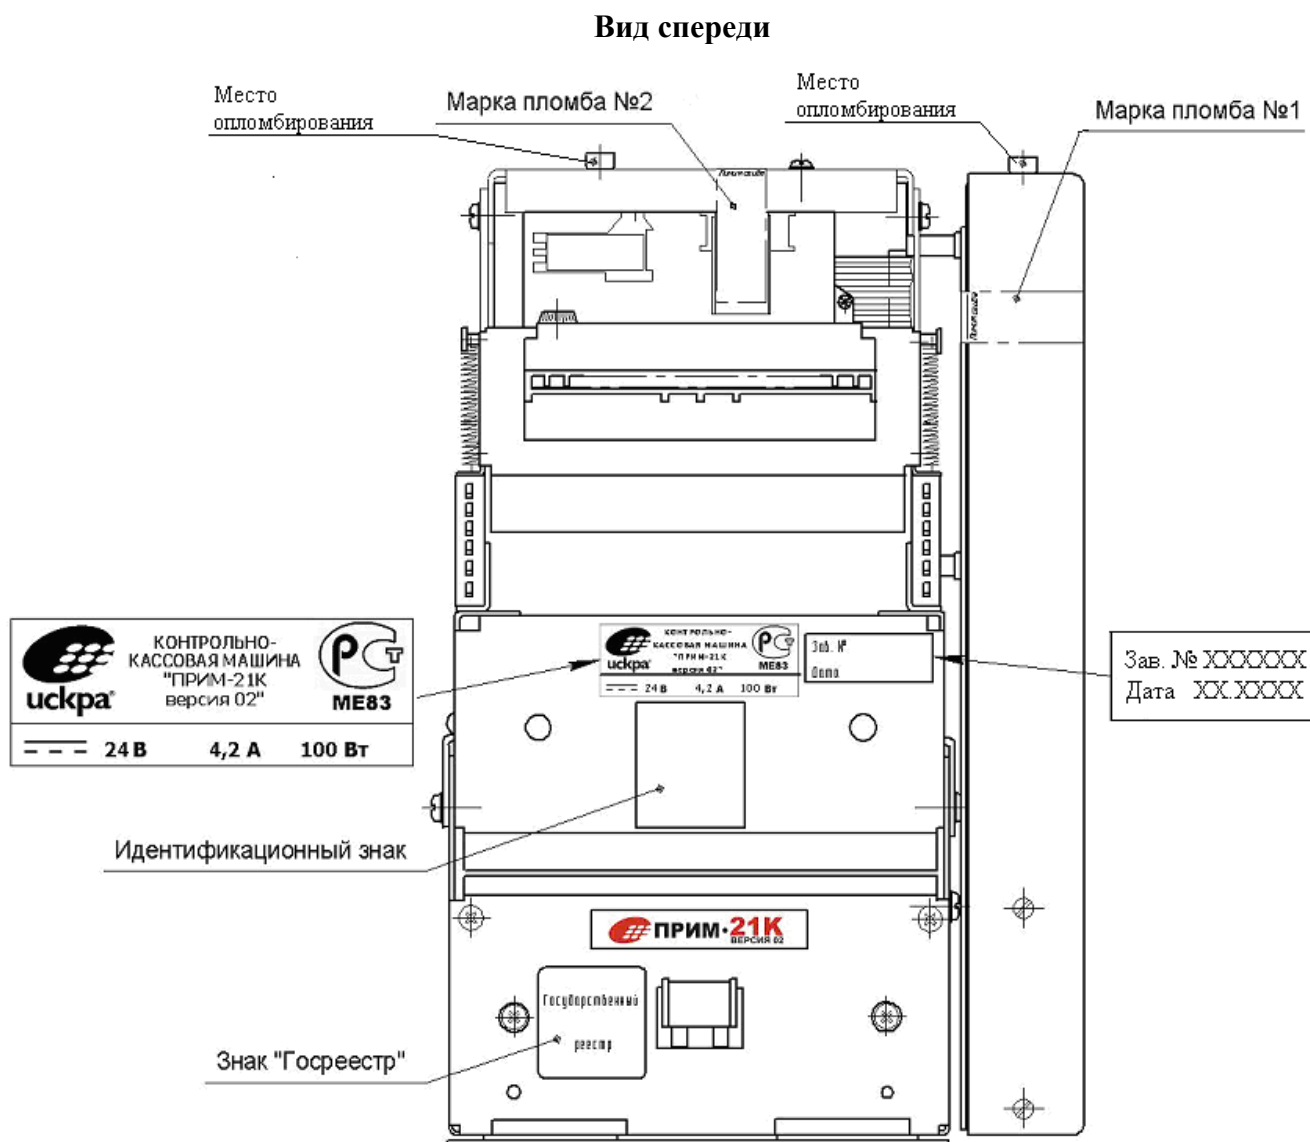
Внешний вид ККМ (вид спереди)
